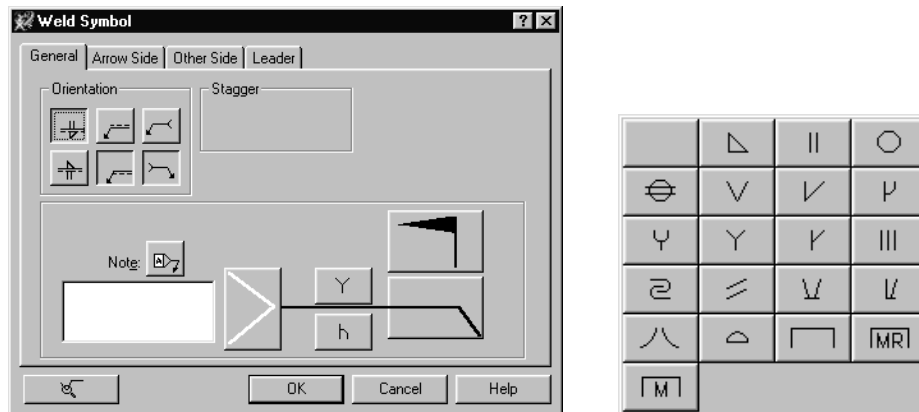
Indicações da Junta Soldada e tipos de Junta
